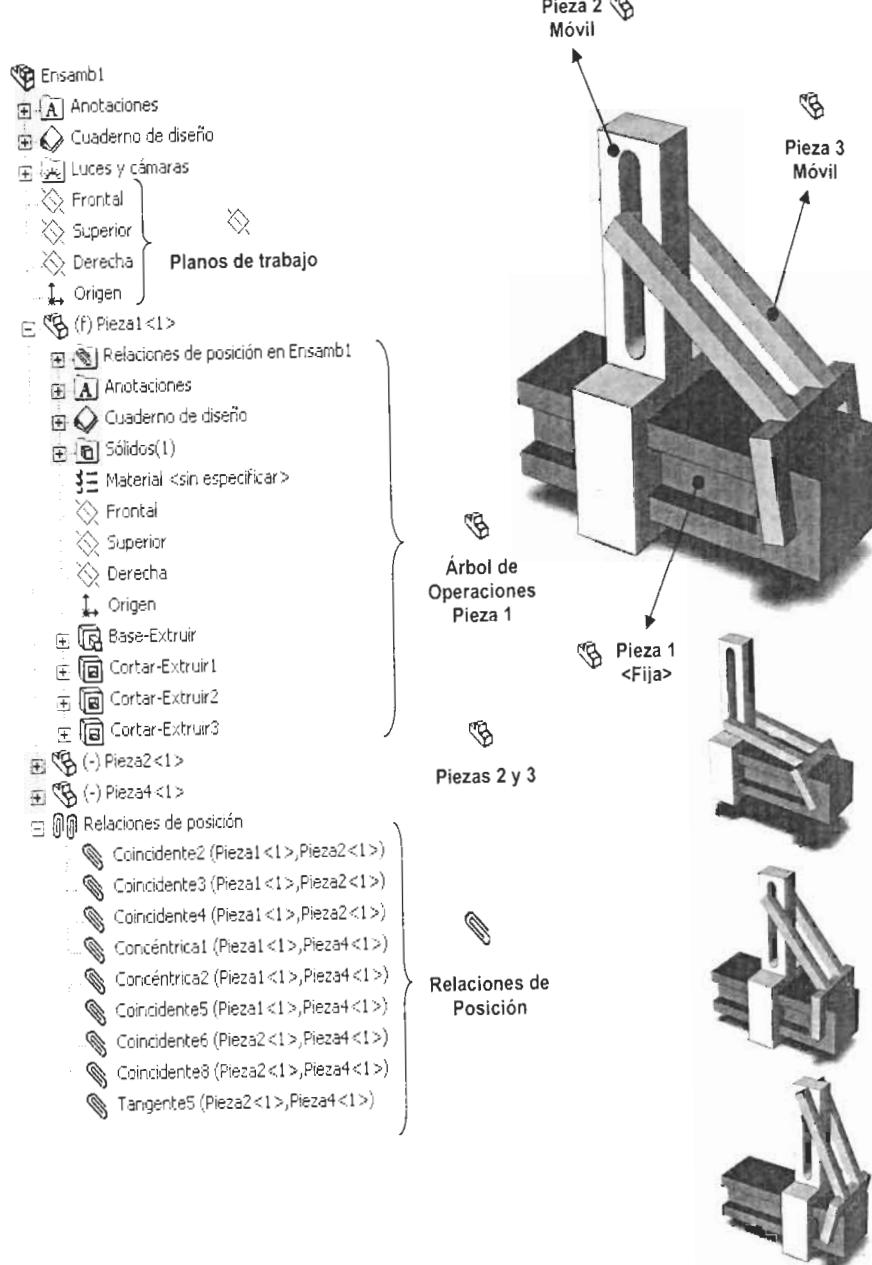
Gestor de Diseño del Módulo de Ensamblajes.
